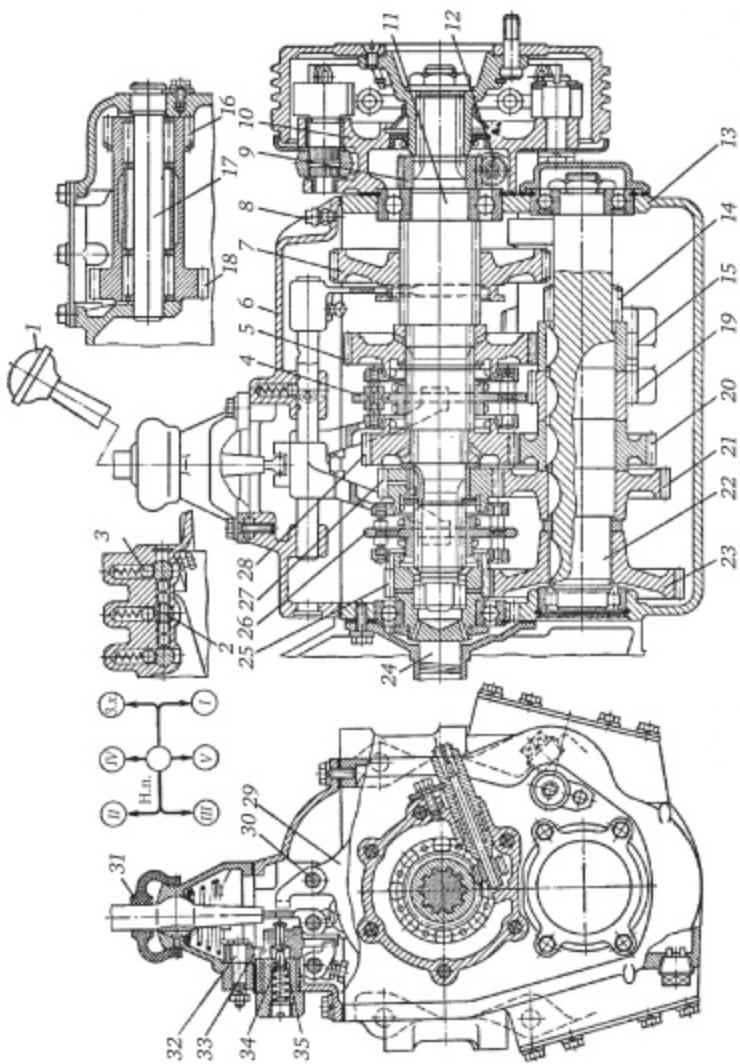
Конструкция 3-вальевой 5-ступенчатой коробки передач грузового автомобиля
